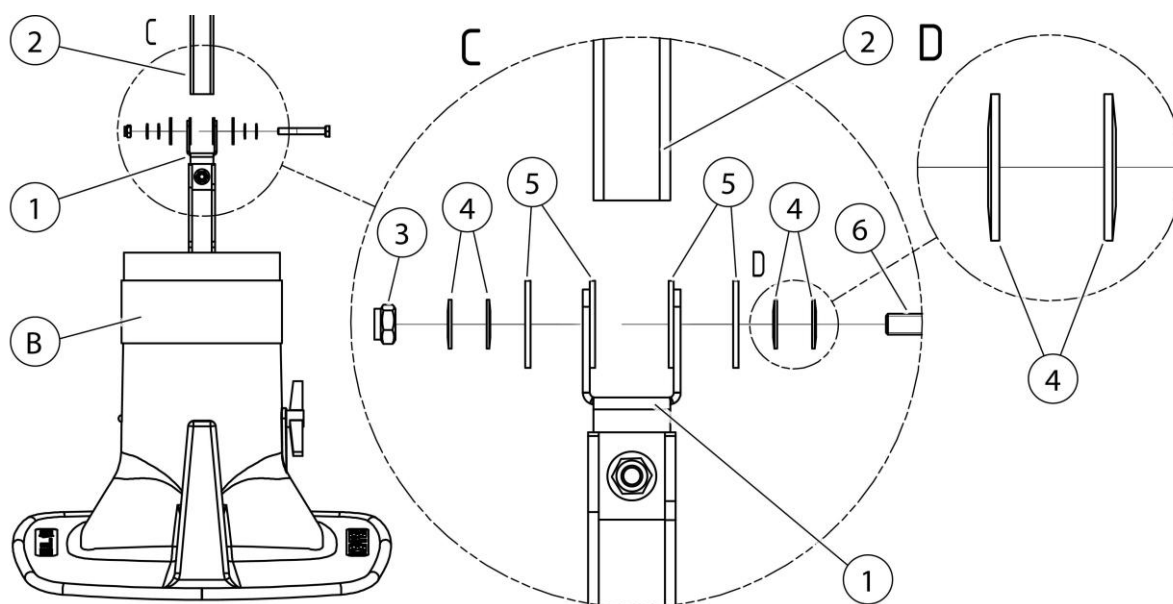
Montaje – Montar el producto con bastidor de soporte
